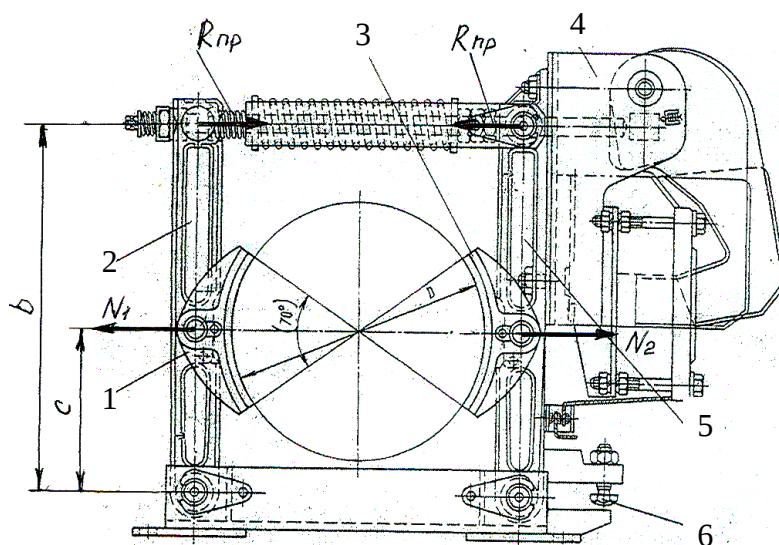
Тормоз двухколодочный короткоходовой. 1, 3 – тормозные колодки, 2, 5 – тормозной рычаг, 4 – электромагнит, 6 – регулировочный винт
